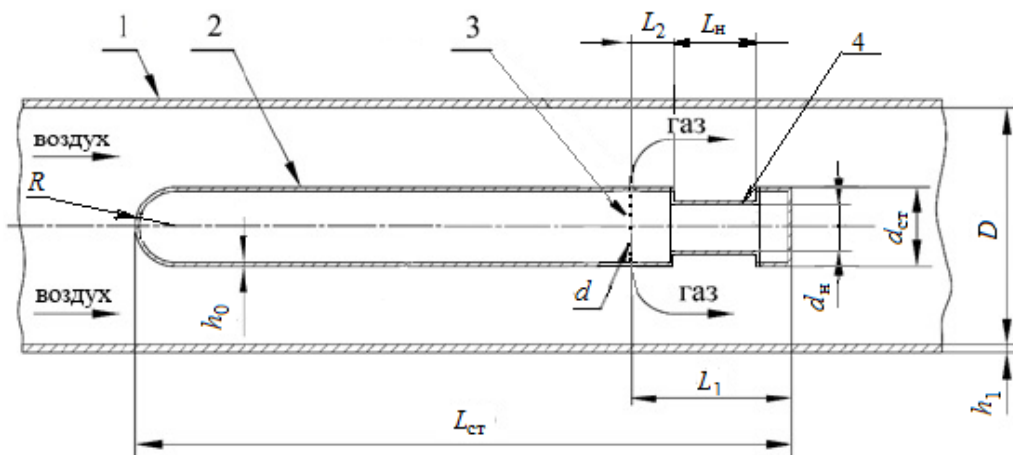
Поздовжній переріз циліндричного стабілізаторного пальника:
